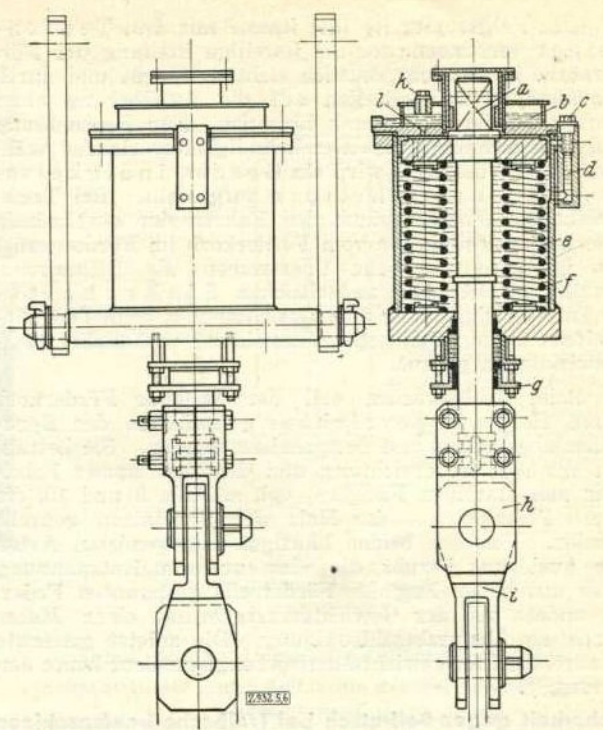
und 6. Stoßdämpfer für schwere Seilbeanspruchung.
